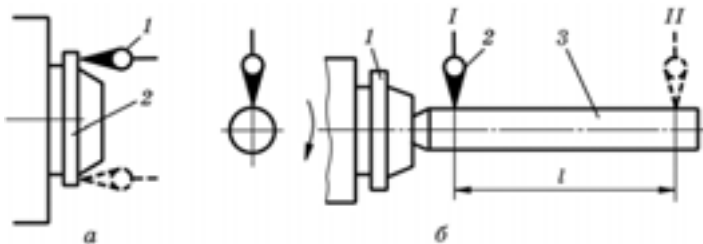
Схеми визначення торцевого биття опорної поверхні (а) і радіального биття внутрішньої центрувальної поверхні (б) шпинделя передньої бабки
